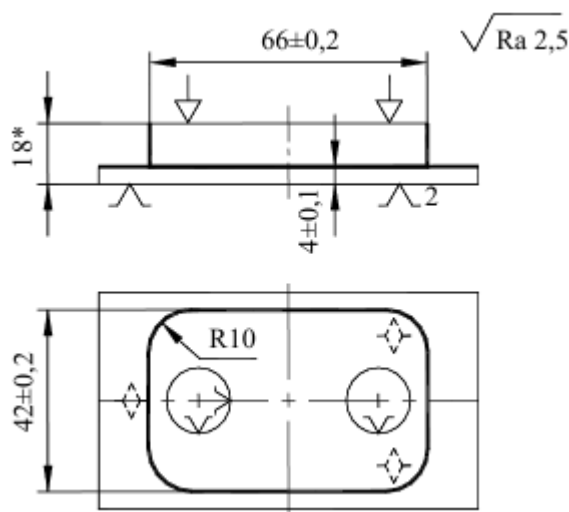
Операційний ескіз на фрезерну операцію для обробки зовнішнього контуру
